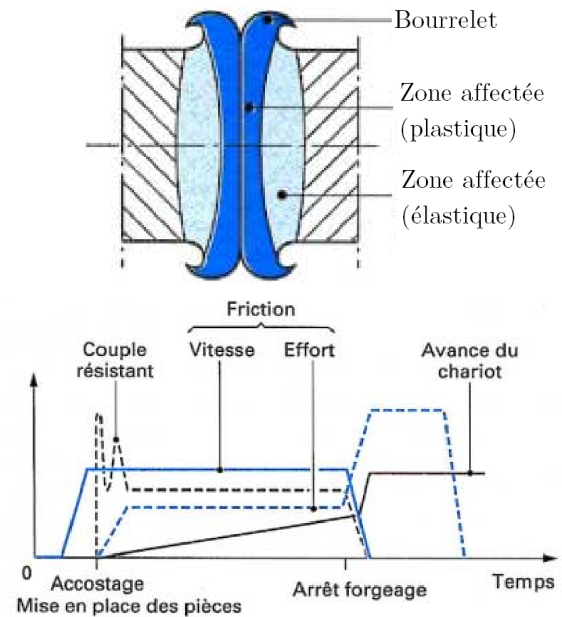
Soudage par friction : description du bourrelet de soudage et évolution des paramètres de soudage [38].
